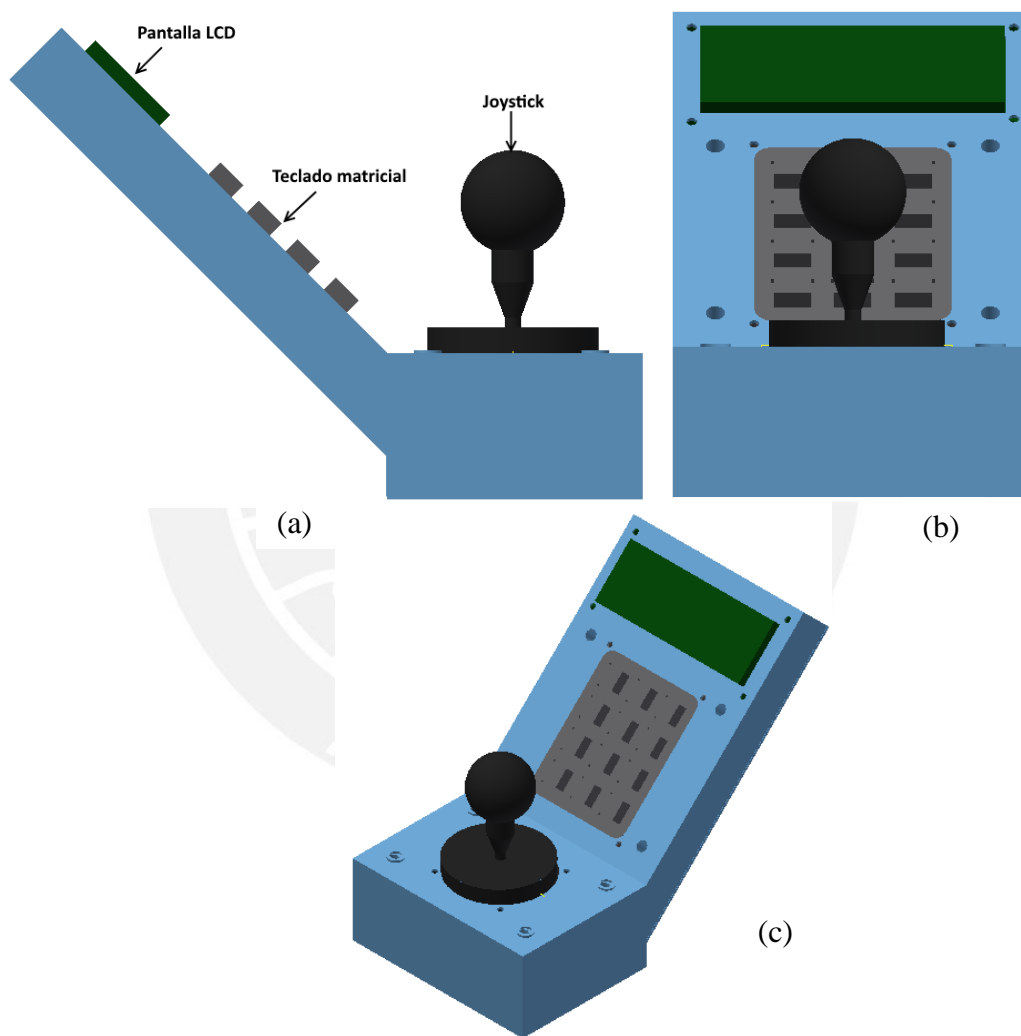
Mando de control (a) Vista lateral, (b) Vista frontal, (c) Vista isométrica
